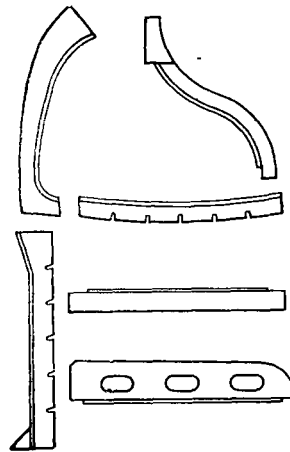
Типы составных сварных балок корпуса
